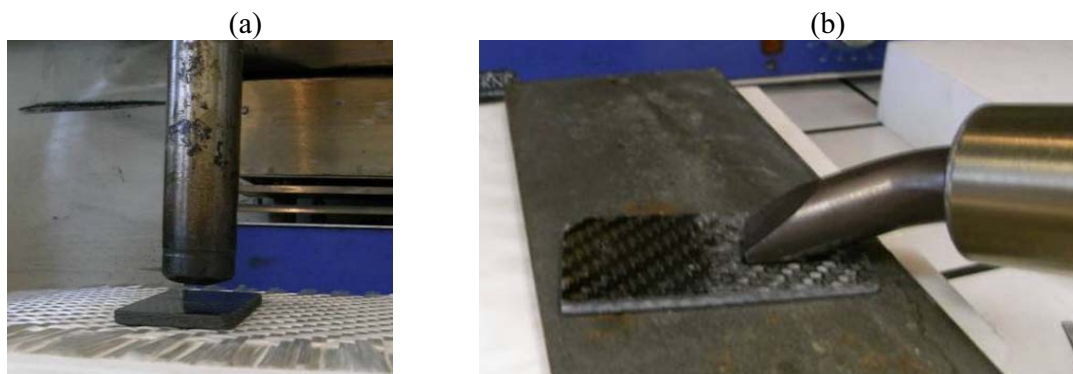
Traitement de surface thermique ; (a) sans contact, décapeur thermique ;(b) avec contact, fer à souder.
